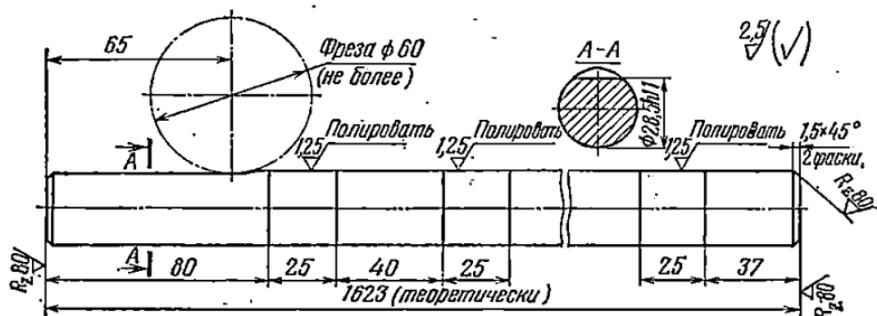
Заготовка коленчатой оси, подготовленная к шлифке.
